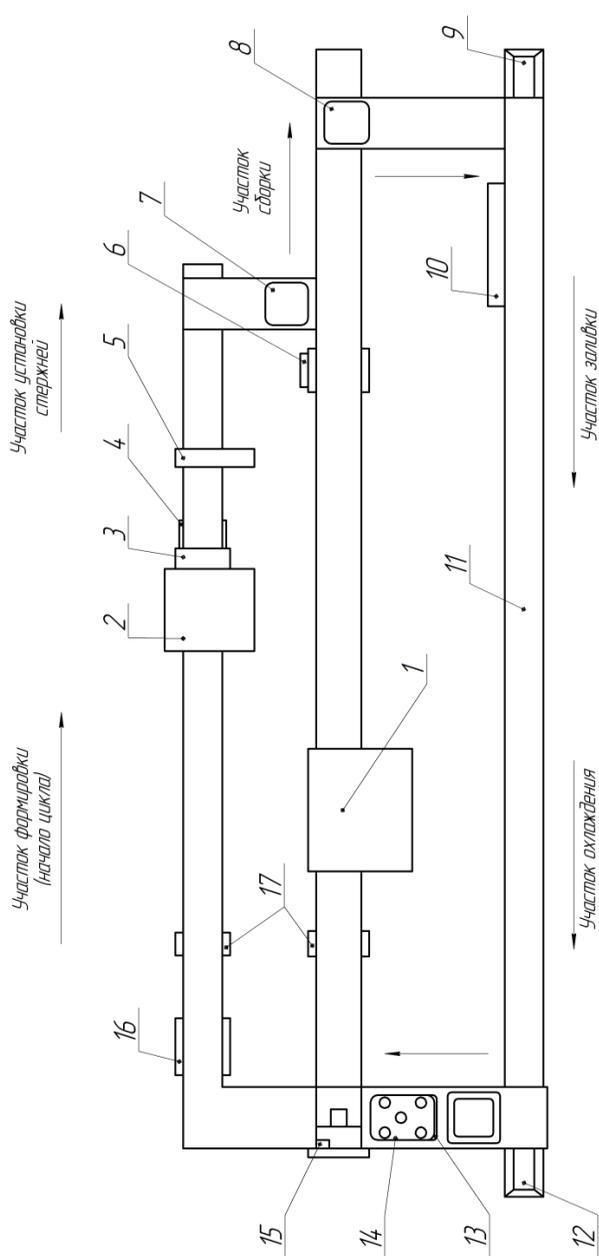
Автоматическая линия для формовки и выбивки опок: 1 – пресс-автомат формовочный пневморычажный верхних полуформ; 2 – пресс-автомат формовочный пневморычажный нижних полуформ; 3 – механизм сверления вентиляционных отверстий; 4 – кантователь нижних полуформ; 5 – механизм срезы смеси нижних полуформ; 6 – кантователь верхних полуформ; 7 – сборщик форм; 8 – кантователь; 9 – механизм подъема подложных плит; 10 – механизм нагружения форм; 11 – конвейер литейный роликовый приводной; 12 – механизм опускания подложных плит; 13 – механизм выдвигания кома; 14 – решетка выбивная инерционная проходная; 15 – распаровщик опор; 16 – кантователь нижних опок; 17 – механизм очистки опок
